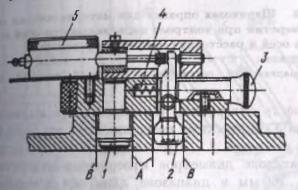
Схема контроля межцентрового расстояния двух отверстий
